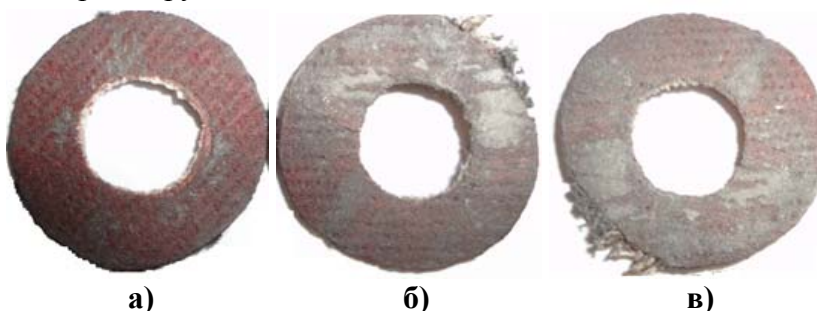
Шлифовальный инструмент (шкурки) с выполненным отверстием для выхода продукта обработки
